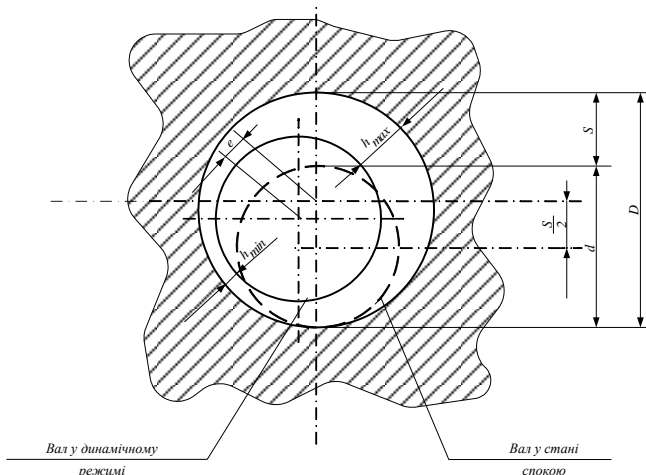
Розрахункова схема і основні параметри підшипника ковзання
